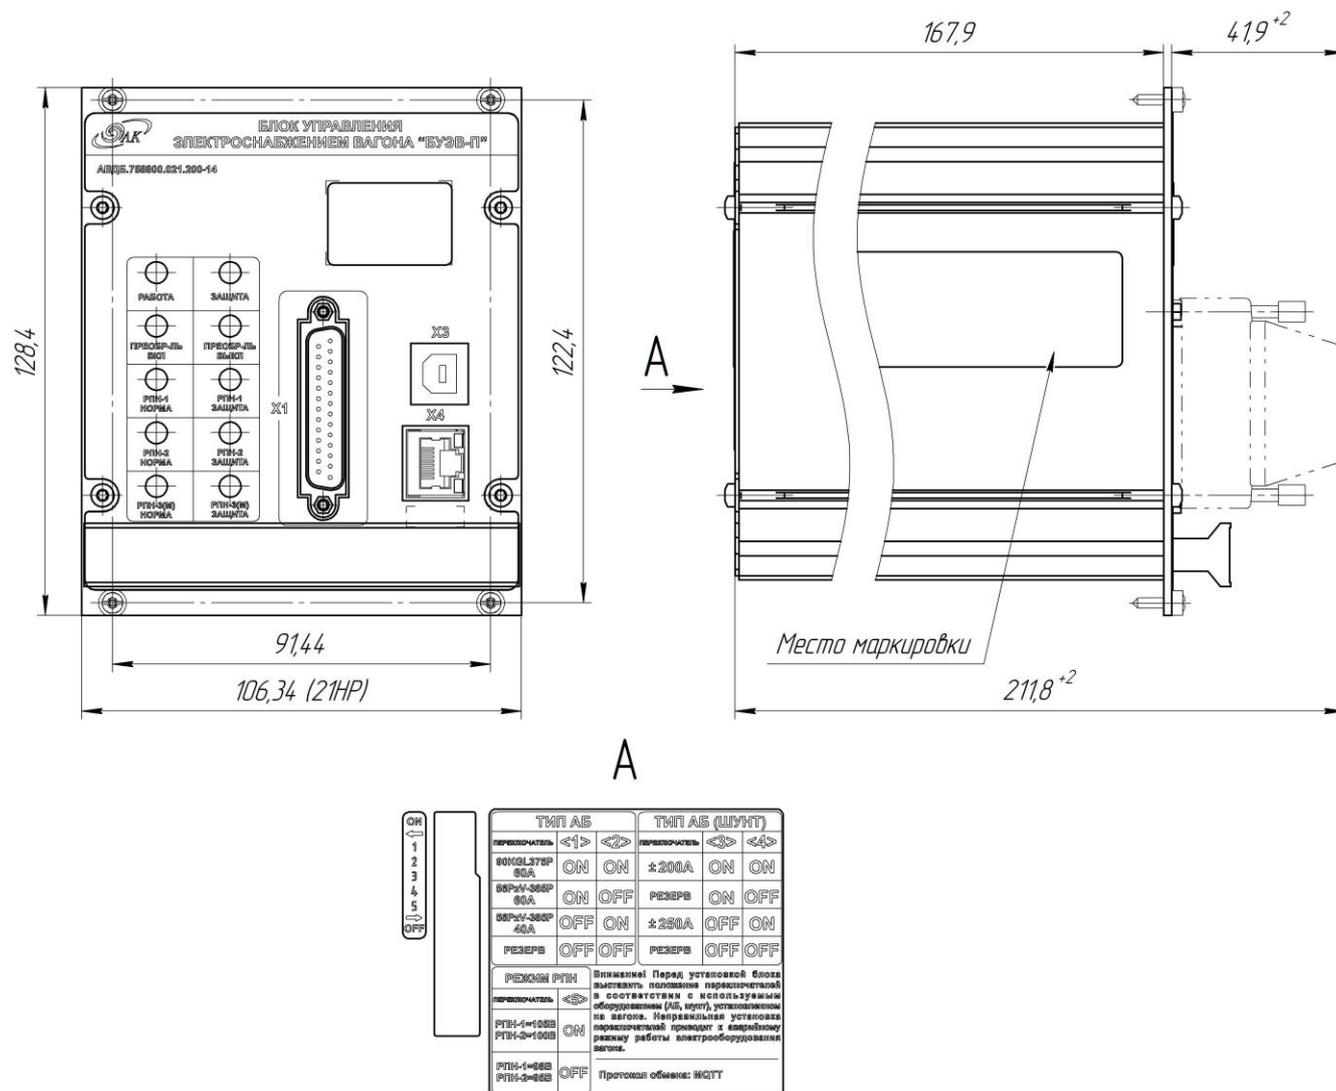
Габаритные и установочные размеры БУЭВ-П
